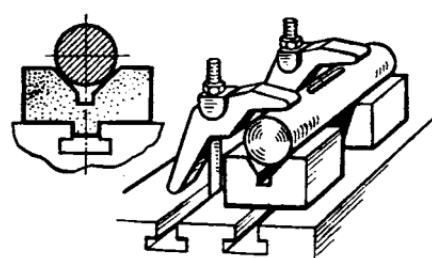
Закрепление вала в призмах для фрезерования паза.
